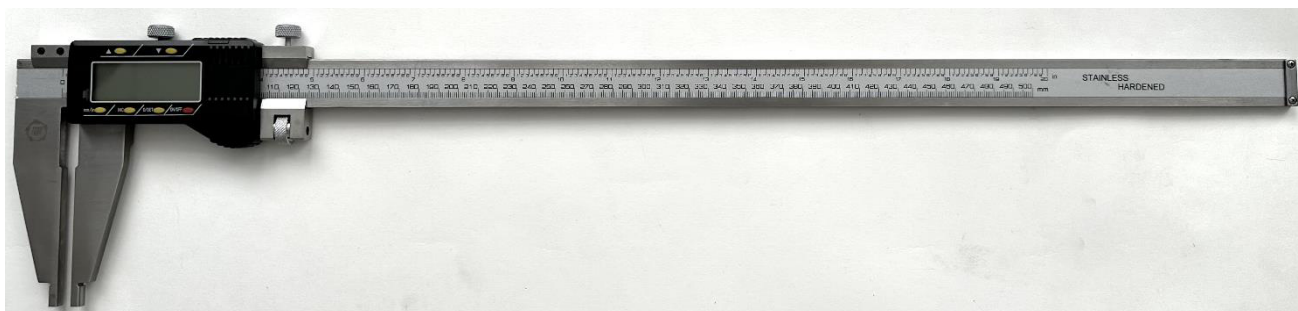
Общий вид штангенциркулей ШЦЦ типа III
